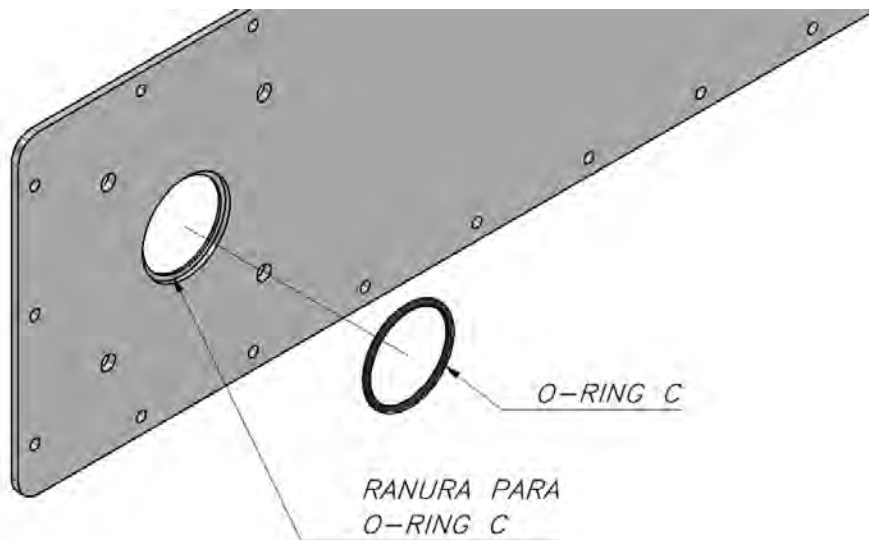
Ensamble del sellado dinámico para el eje de transmisión
